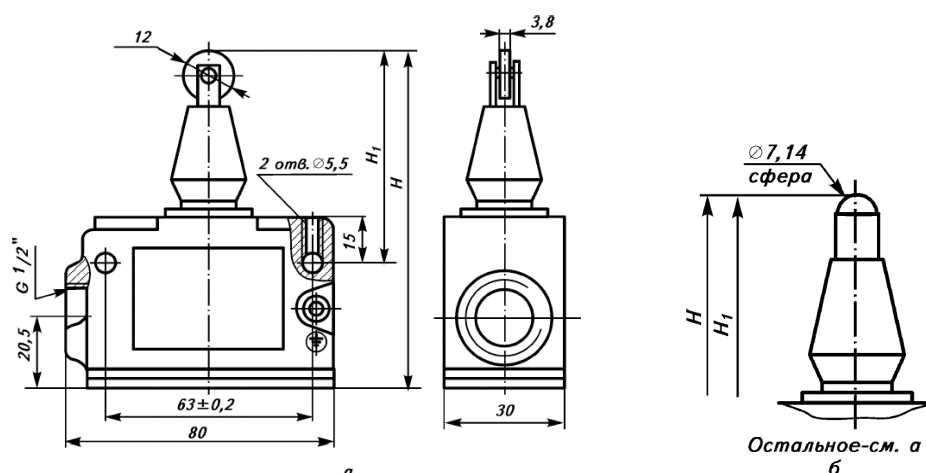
Габаритные, установочные и присоединительные размеры микровыключателей со степенью защиты IP54 с комбинированным креплением на поверхности, с монтажом проводов винтами или пайкой с приводом:
